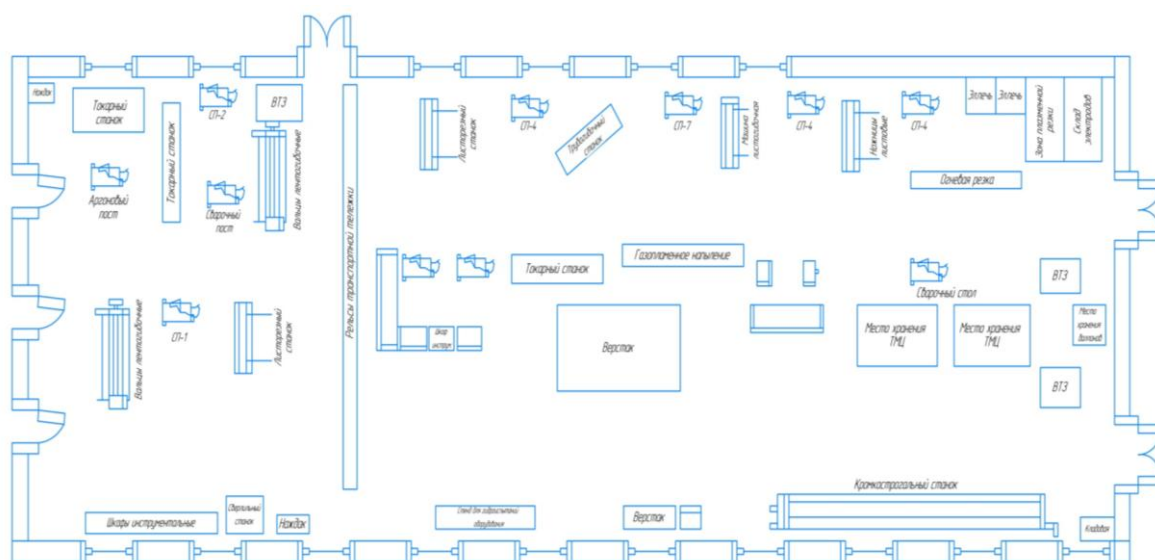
План-схема сварочно-монтажного участка РМЦ
